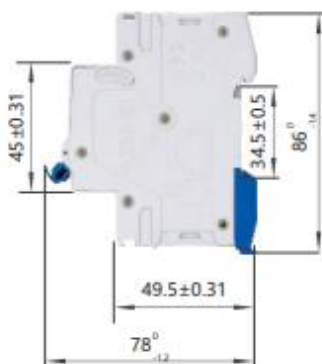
Dimensiones Generales y de Montaje del Interruptor Termomagnético [24]
